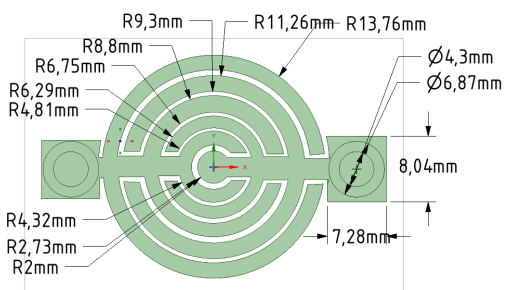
Nákres součástky s kruhovými elektrodami v CAD programu
